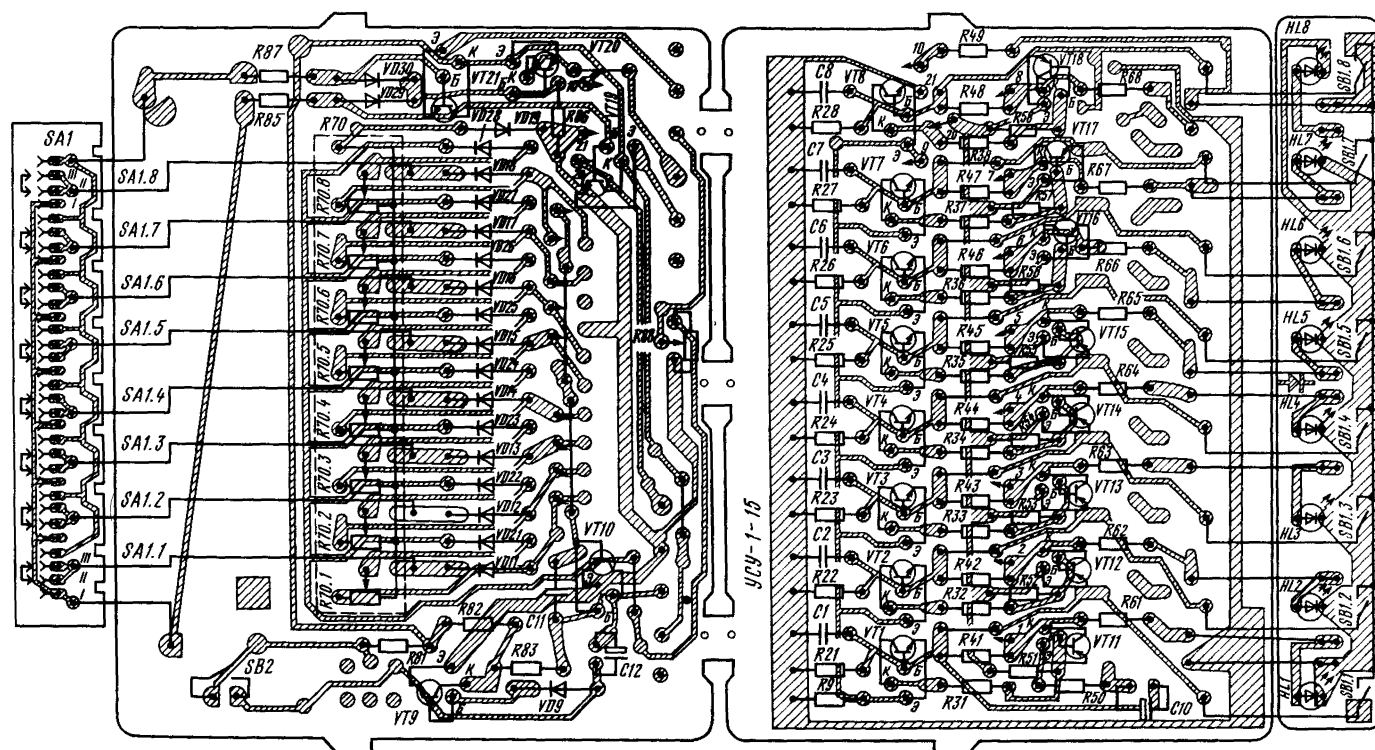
Электромонтажные схемы печатных плат УСУ-1-15
